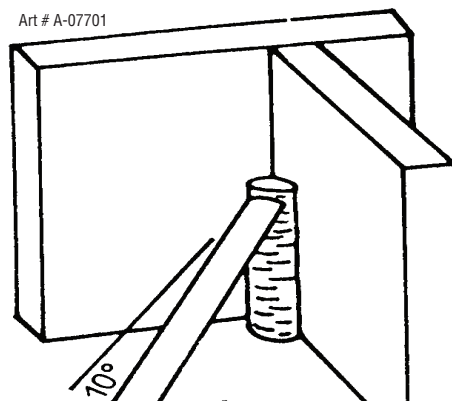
Soudure d'angle Verticale à un seul passage
